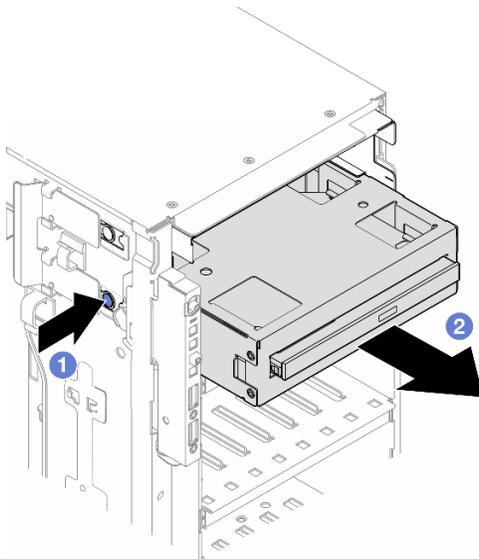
Entfernen einer Adapterbaugruppe für eine 5,25-Zoll-Laufwerkposition
